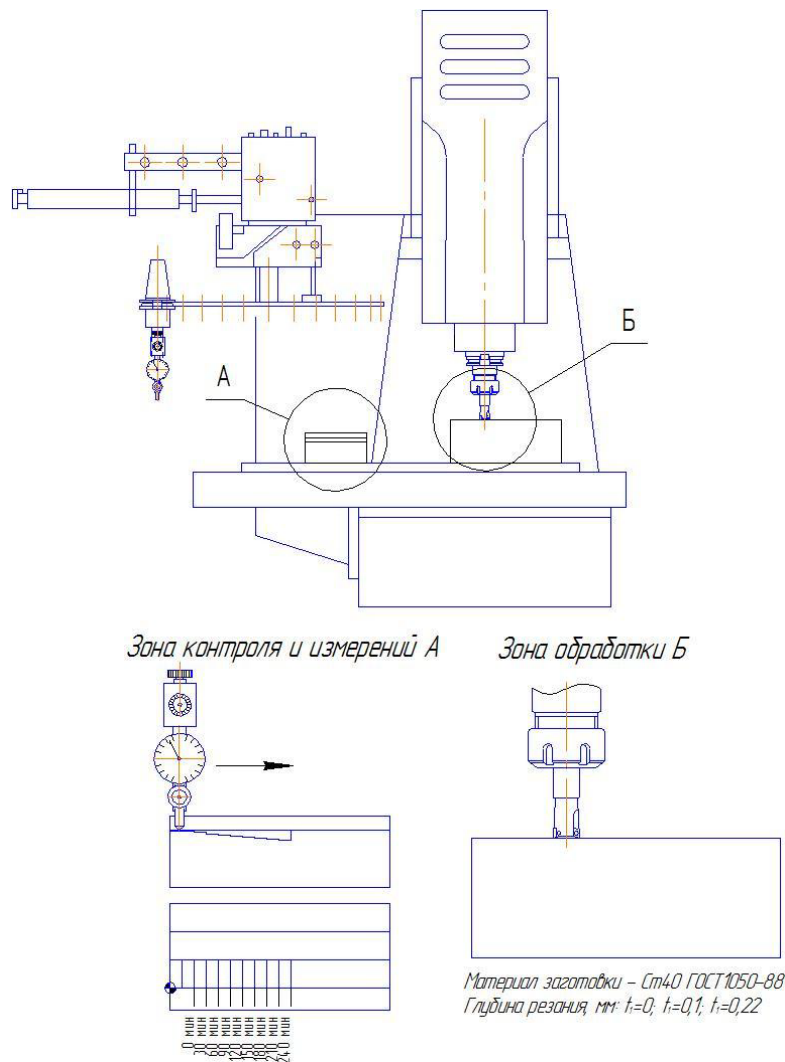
Схема випробувань верстат під навантаженням з обробкою металу [8]
